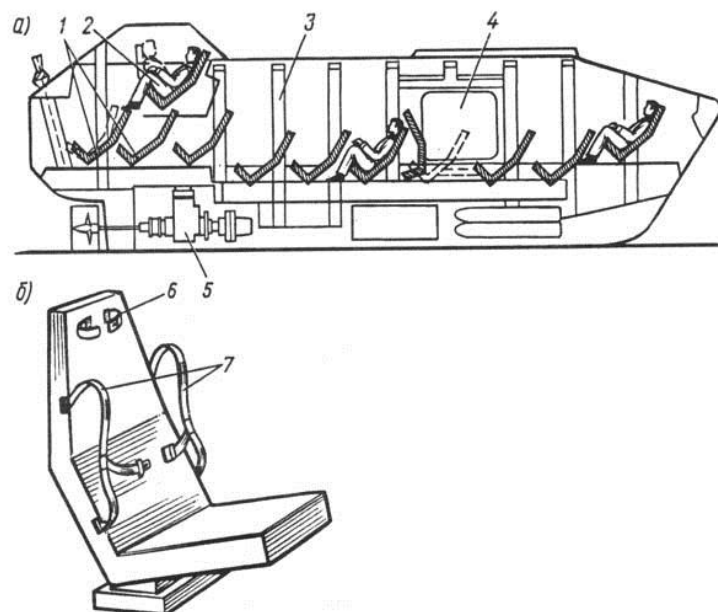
Шлюпка свободного падения: а – конструкция; б – кресло-амортизатор; 1 – кресла; 2 – положение человека в момент падения; 3 – усиленный набор; 4 – люк для посадки; 5 – двигатель; б – фиксатор головы; 7 – ремни безопасности
